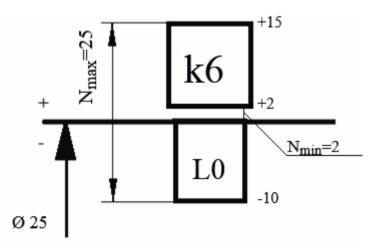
Поля допусков и показатели точности посадки для сопряжения внутреннего кольца подшипника и вала
